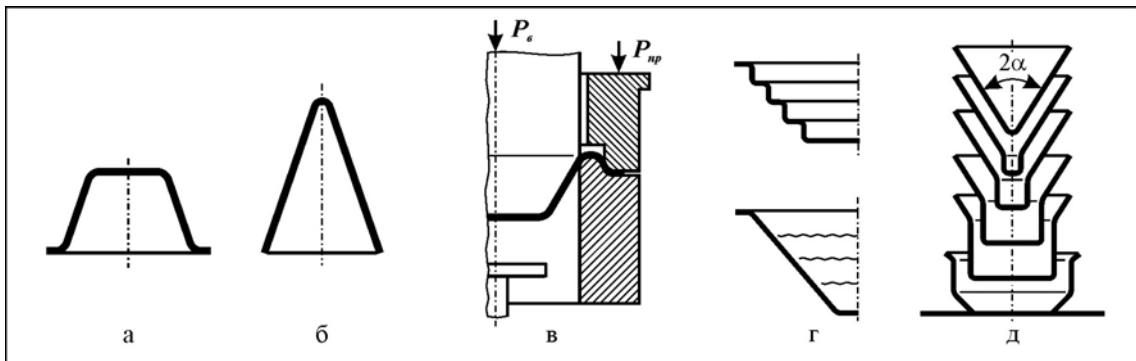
Витягування конічних деталей: а – низька конічна деталь (у вигляді обрізаного конуса); б – висока конічна деталь (гострокінцева, з малим кутом конуса α); в – схема штампа з перетяжним порогом для витягування низької конічної деталі; г – перший спосіб витягування високої конічної деталі; д – другий спосіб витягування високої конічної деталі
